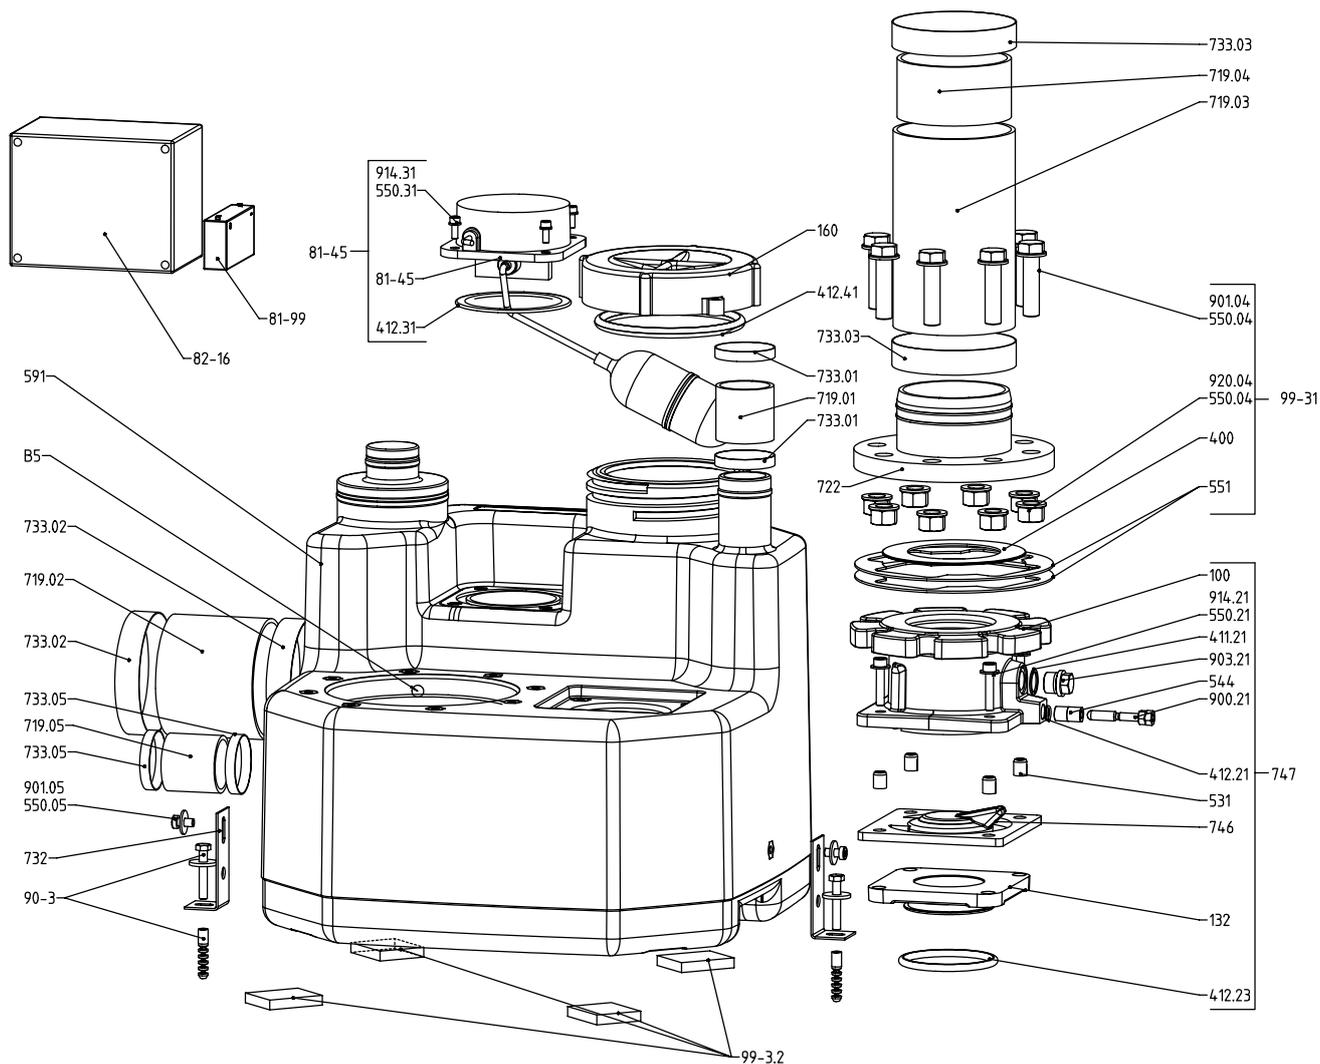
Детализированное изображение mini-Compacta U60, U100 - сборный резервуар
